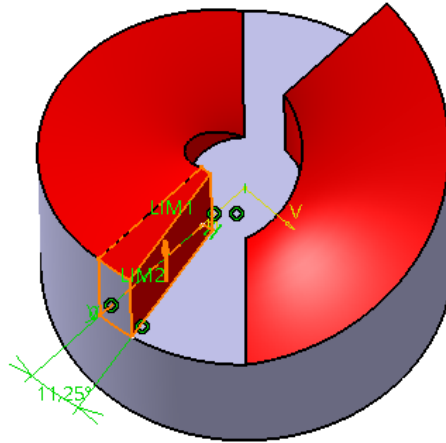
3D planos horizontales de impacto del engranaje superior.
